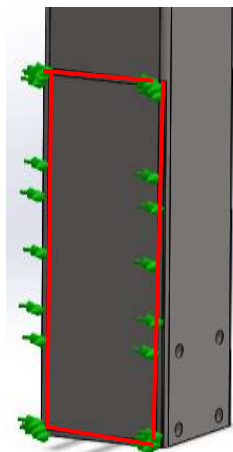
Localización de soldadura de la placa de sujeción de las guías con la columna
